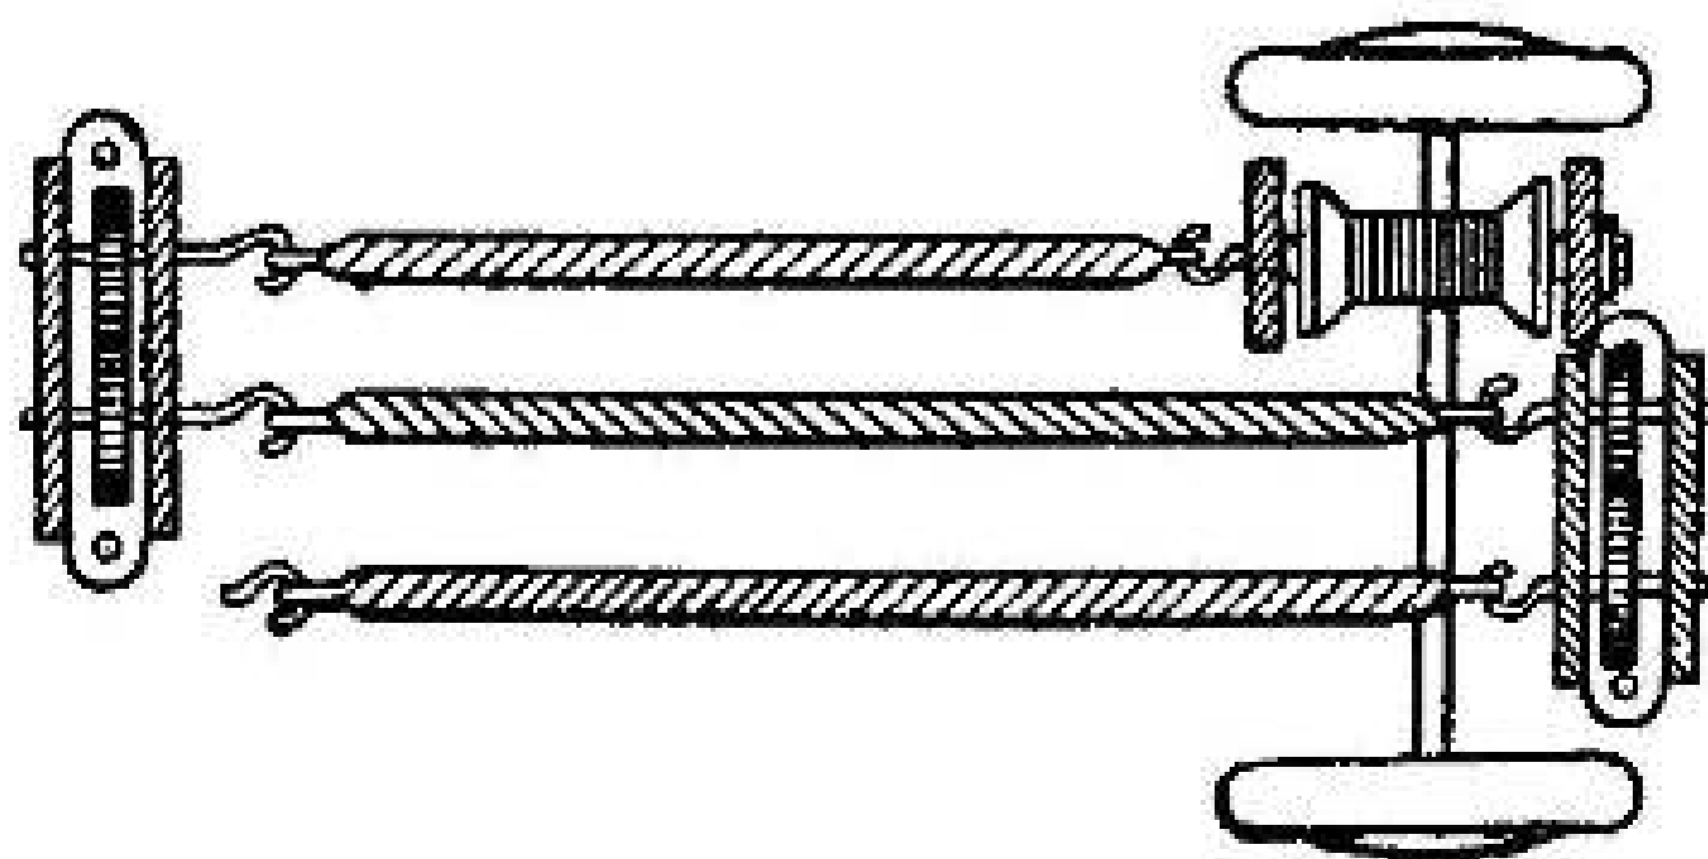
Схема утроенного резинового двигателя с двумя шестеренчатыми редукторами
